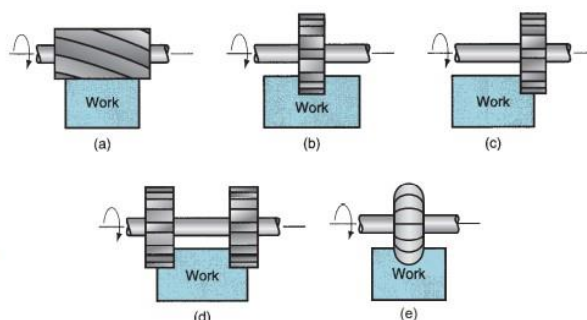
Operações de fresagem periférica (adaptado de [7])
